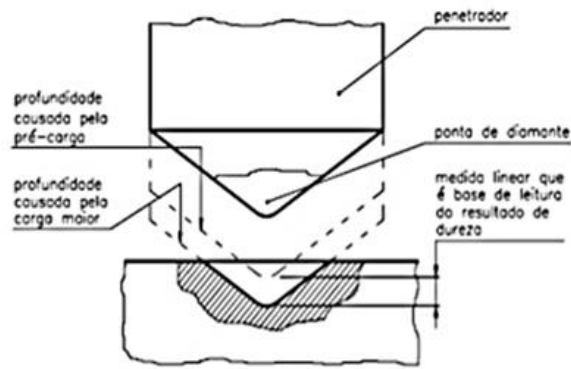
Representação esquemática da profundidade produzida por um penetrador cônico. [27]
